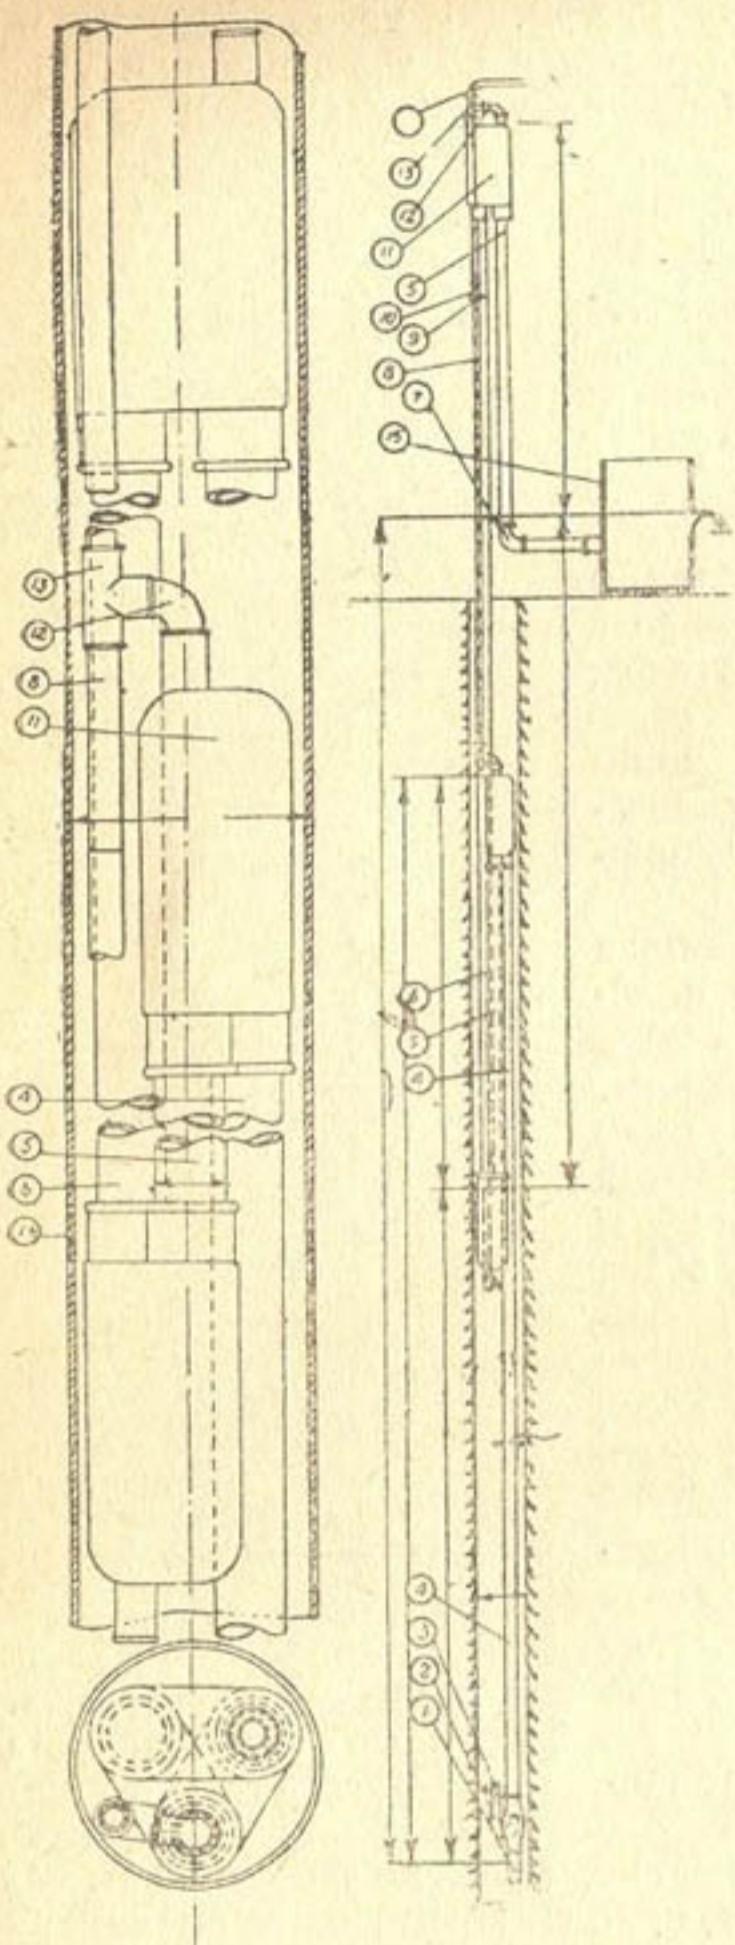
Всасывающий двухступенчатый эрлифт сист. Алексеева.
